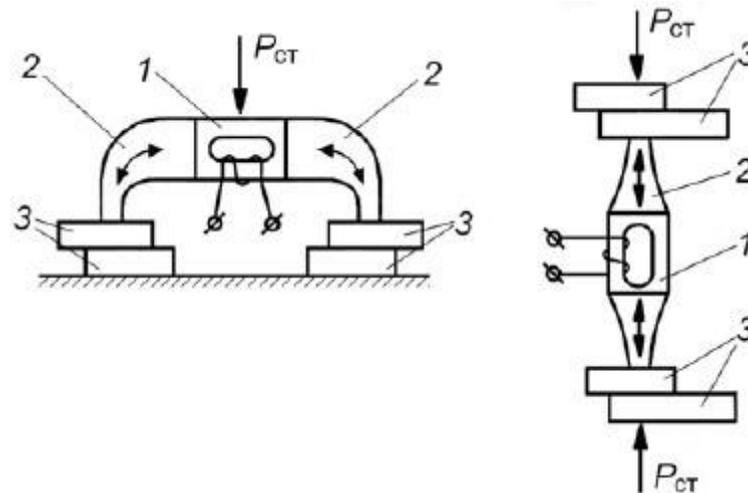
Схемы сварки с двусторонним отбором энергии от преобразователя: 1 – преобразователь; 2 – волновод; 3 – свариваемые детали
